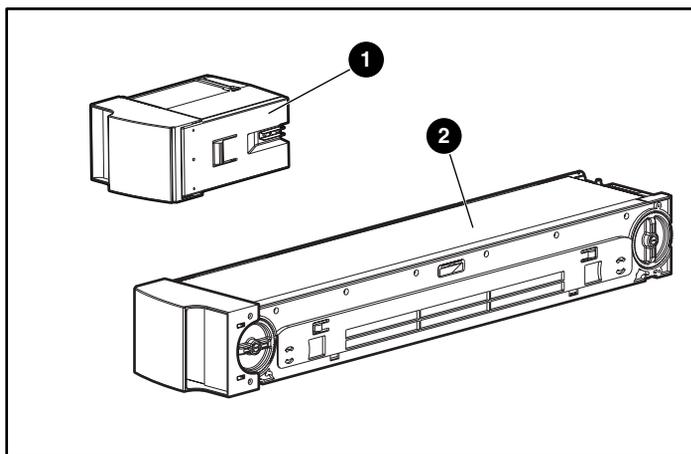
Caricatore vuoto ❶ e caricatore ❷
